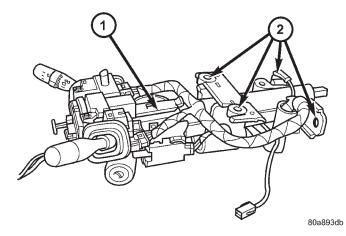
MONTAJE DE LA COLUMNA DE DIRECCION
